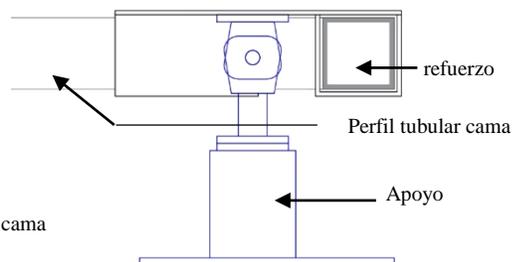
Vista en alzado, refuerzo, cama, apoyo
